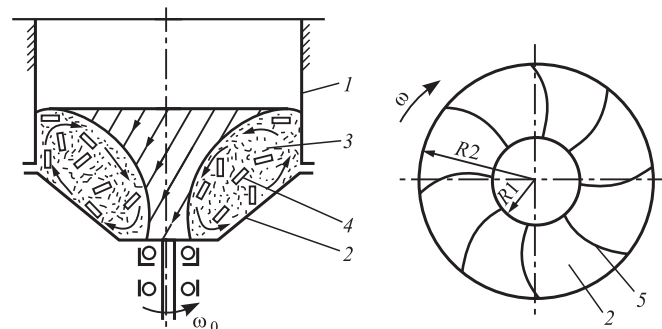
Схема центробежно-ротационной обработки деталей на установках с конической тарелью:
